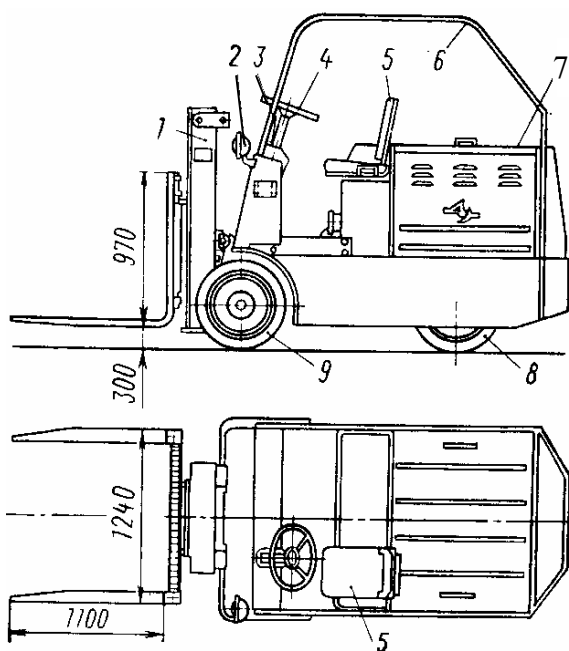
Электропогрузчик ЭП-501-Н с вилочным захватом: 1 – рама подъемника; 2 – фара; 3 – рукоятка; 4 – рулевое управление; 5 – сидение; 6 – кожух кабины; 7 – батарейный ящик; 8 – ведущие колеса; 9 – управляемые колеса
